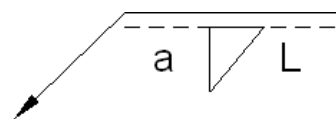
Cordón de soldadura por el lado opuesto a la flecha
